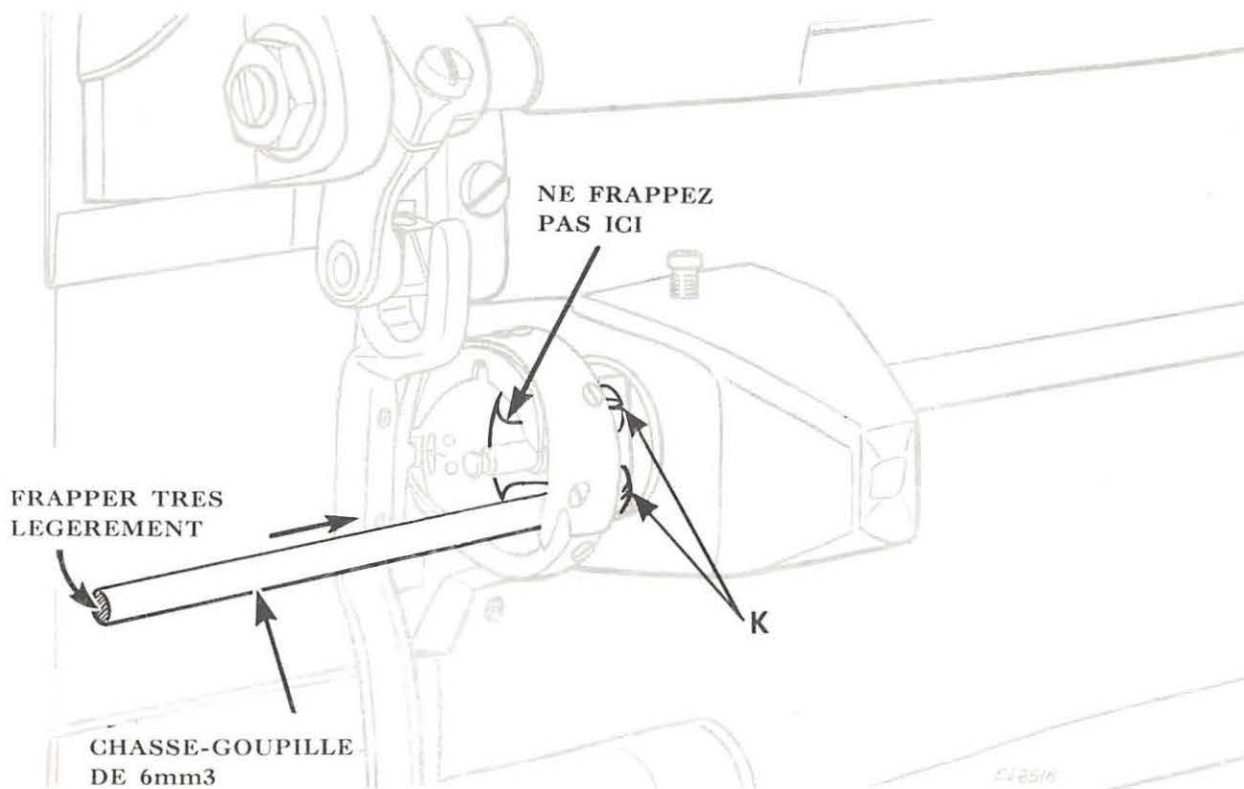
Assemblage de crochet chassé de manière à l'ELOIGNER de l'aiguille
